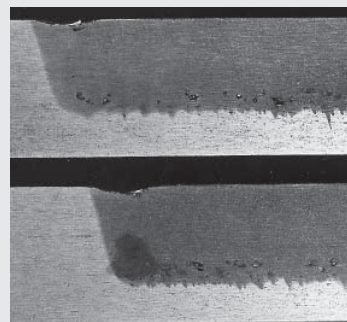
Продольный макрошлиф лазерного сварного шва
